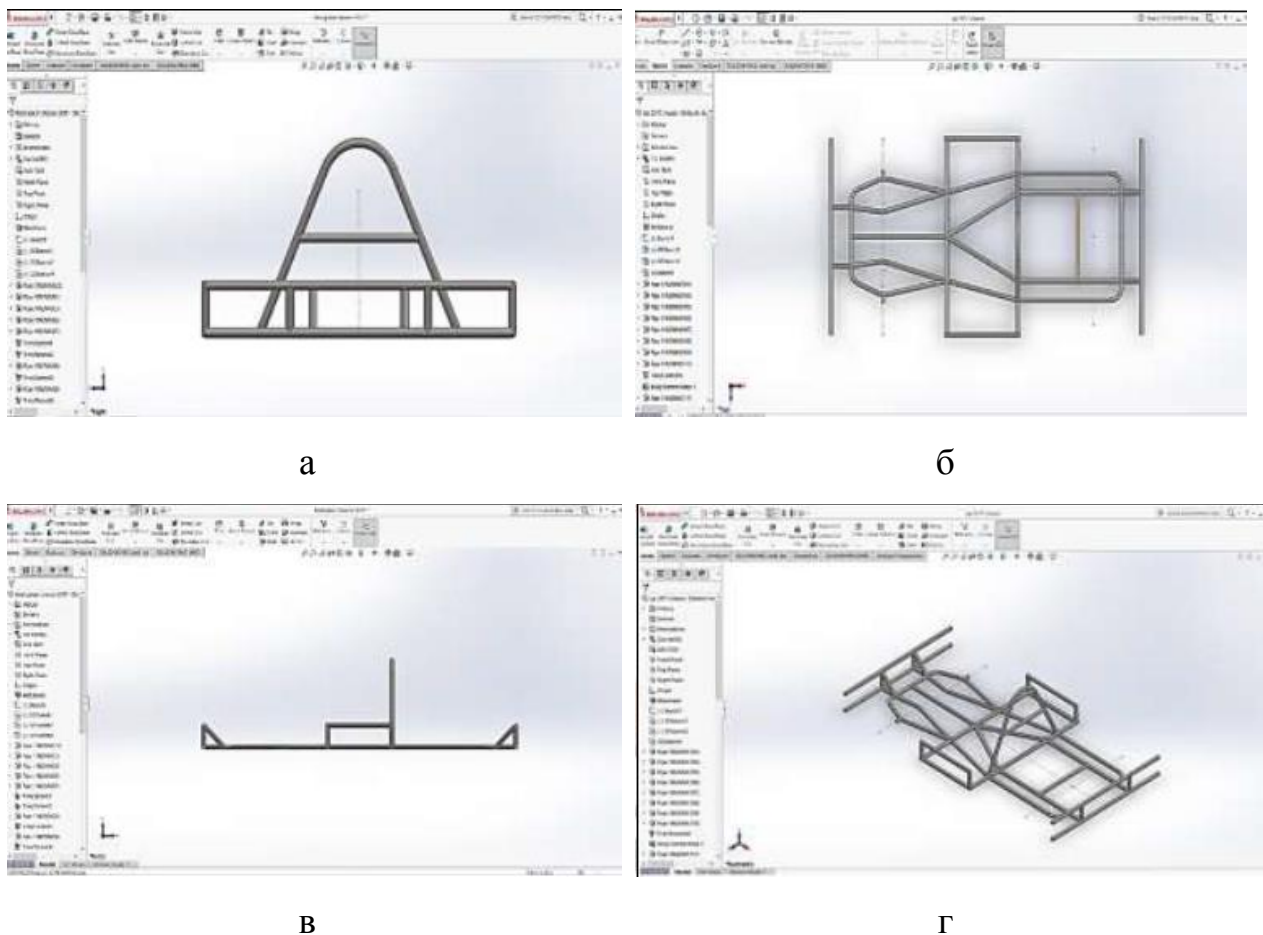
Конструкция рамы: а – фронтальный вид, б – вид сверху, в – вид сбоку, г – изометрический вид
